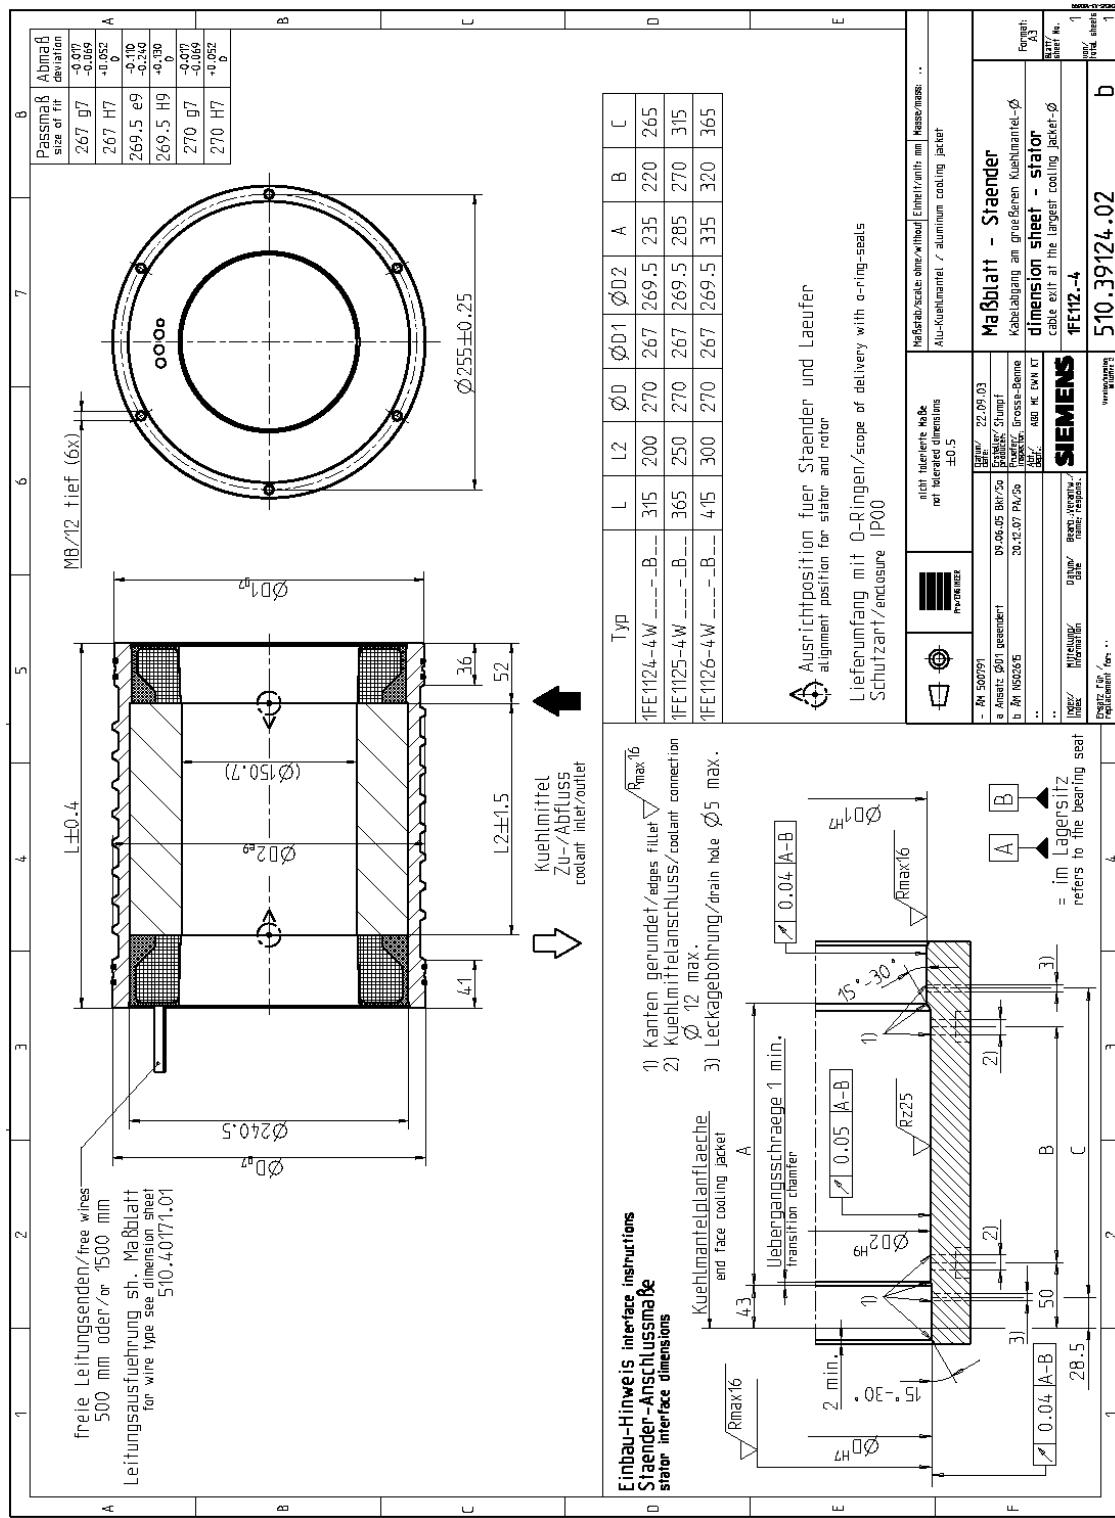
1FE112□-4, Ständer mit Kühlmantel, Kabelabgang am größeren Kühlmanteldurchmesser
